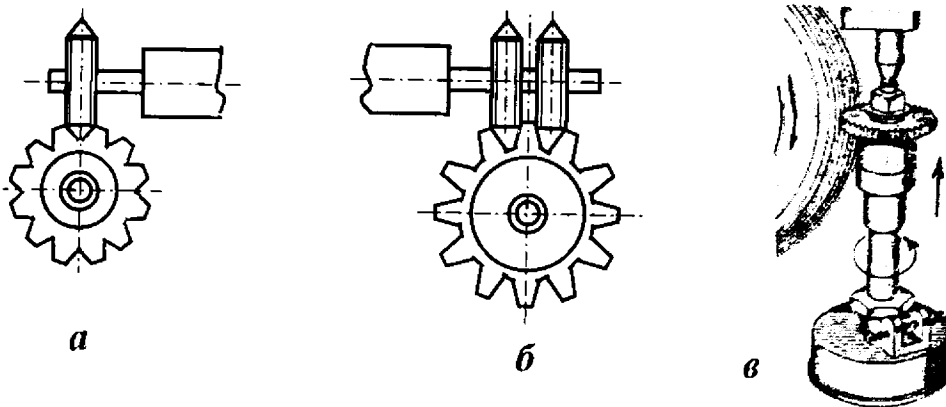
Зубошлифование цилиндрических зубчатых колес: а – на станке 5851 одним конусным кругом; б – двумя абразивными кругами; в – на станке МАТРИКС червячным абразивным кругом
